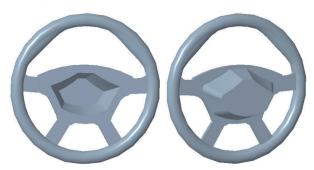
汽车方向盘的三维模型 Fig. 12 3D model of a car steering wheel
